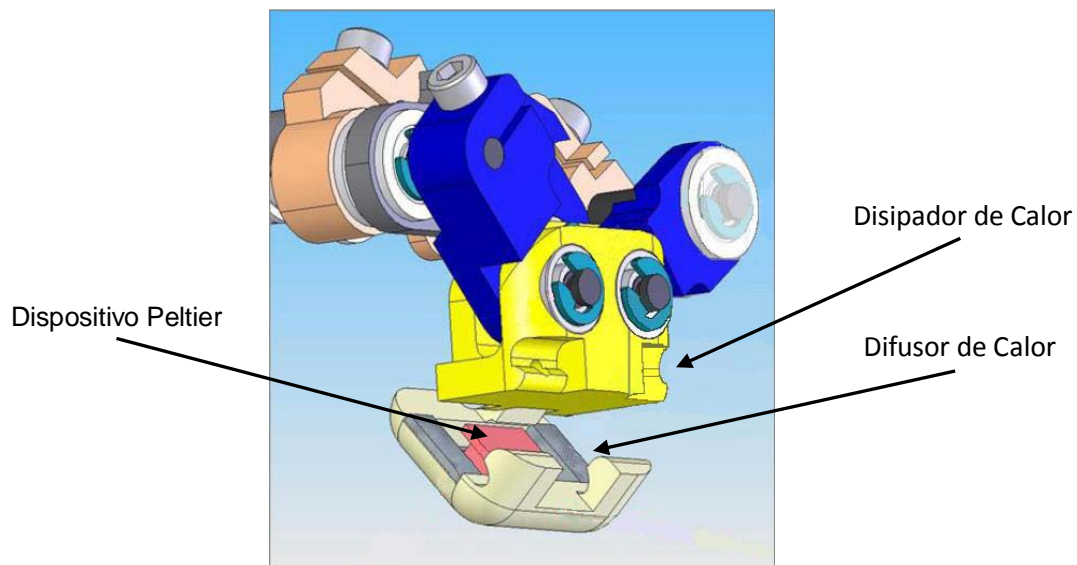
Dibujo en CAD de un sensor de tacto donde se muestran las partes que lo componen [17]
